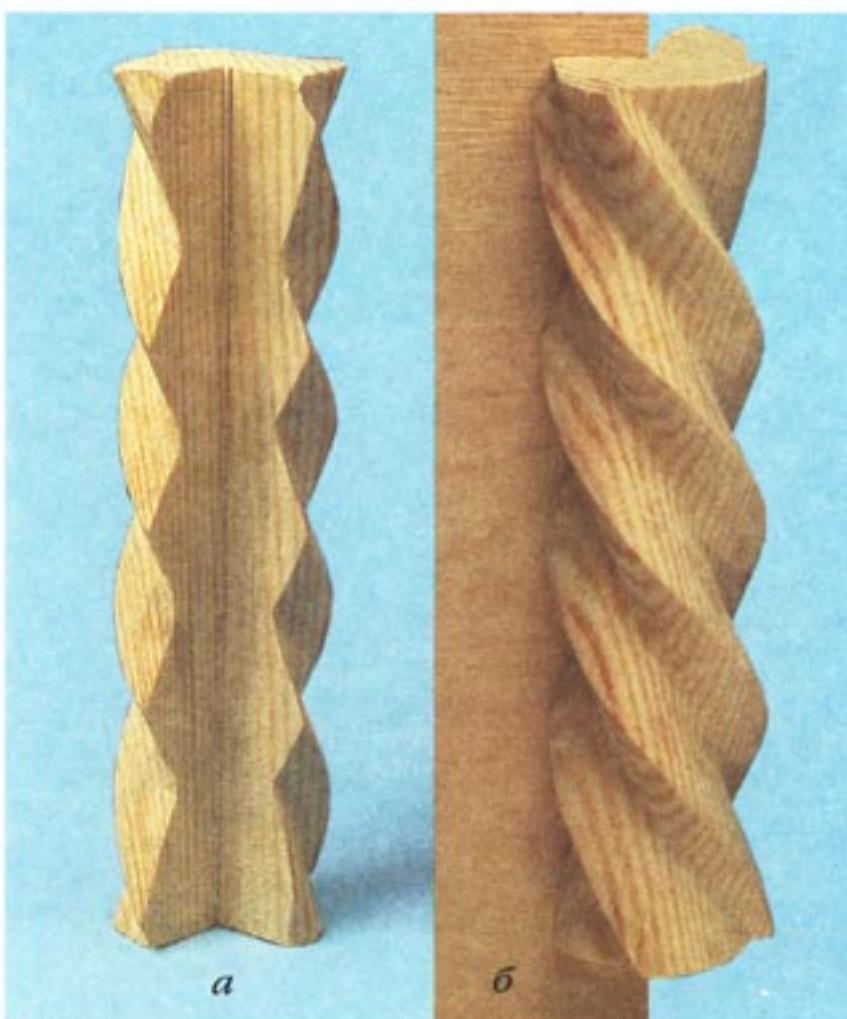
3/4 винта, изготовленные из целого винта: а – вид со стороны ростпуска циркулярной пилой; б – вид при накладке на изделие
